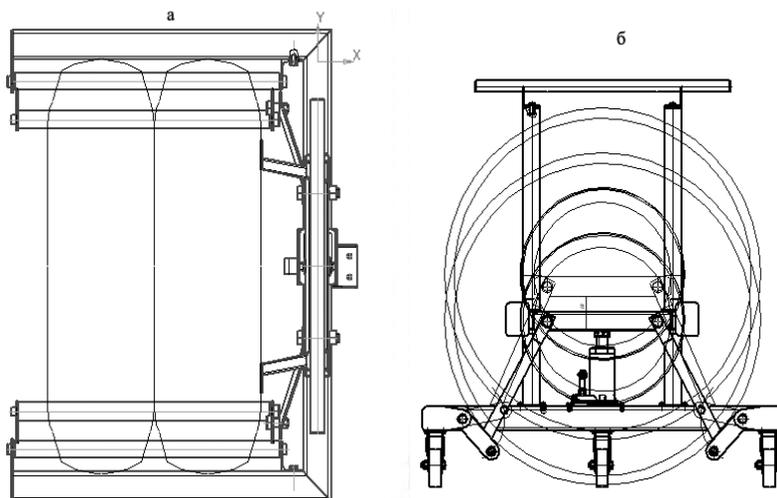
Тележка для монтажа и демонтажа колес: а) вид сверху; б) вид спереди
